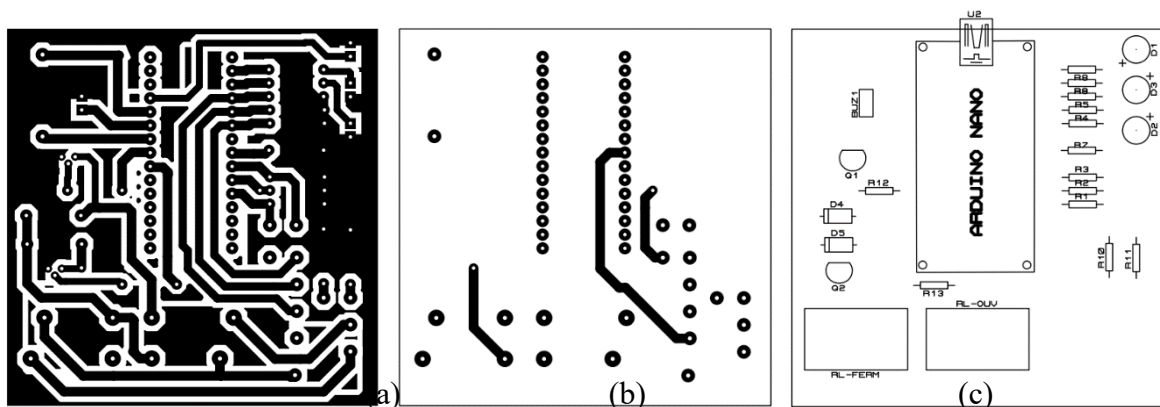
(a) PCB botton, (b) PCB top et (c) top resist
